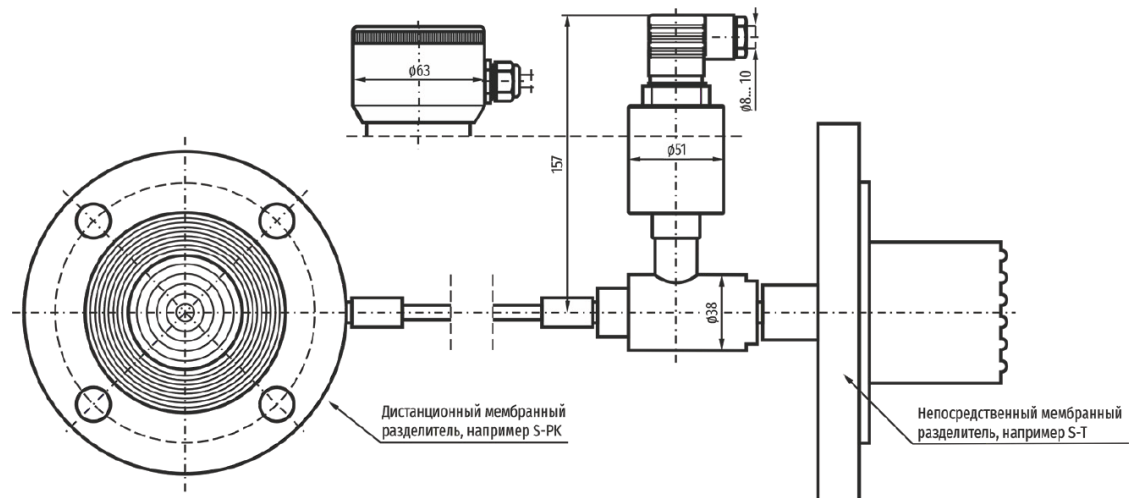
Преобразователь давления измерительный APR-2200 с дистанционным и непосредственным разделителями. Внешний вид, габаритные размеры
